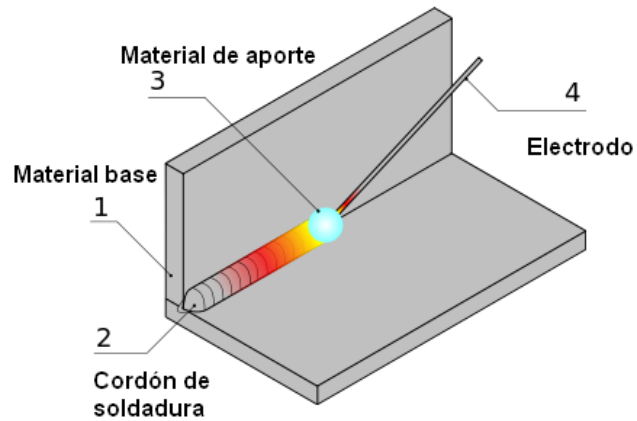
33 Esquema de soldadura eléctrica
